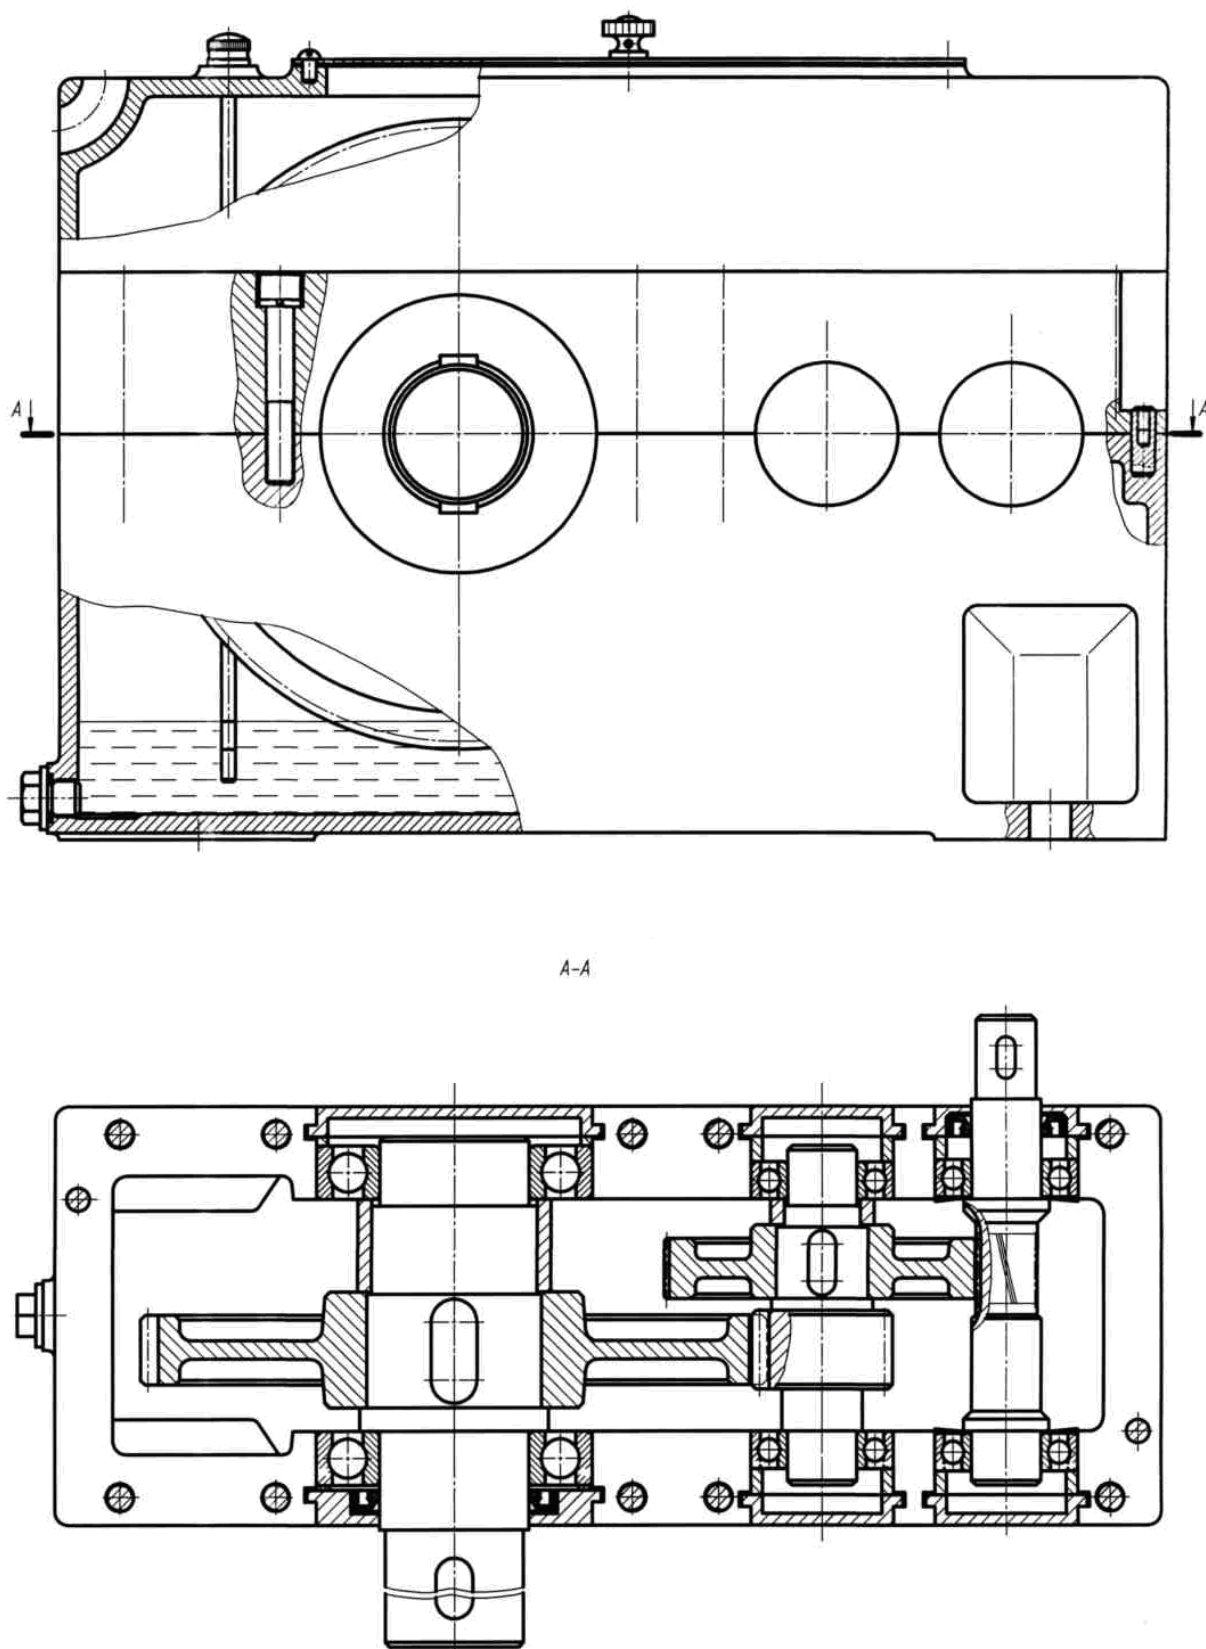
Редуктор двухступенчатый цилиндрический горизонтальный
